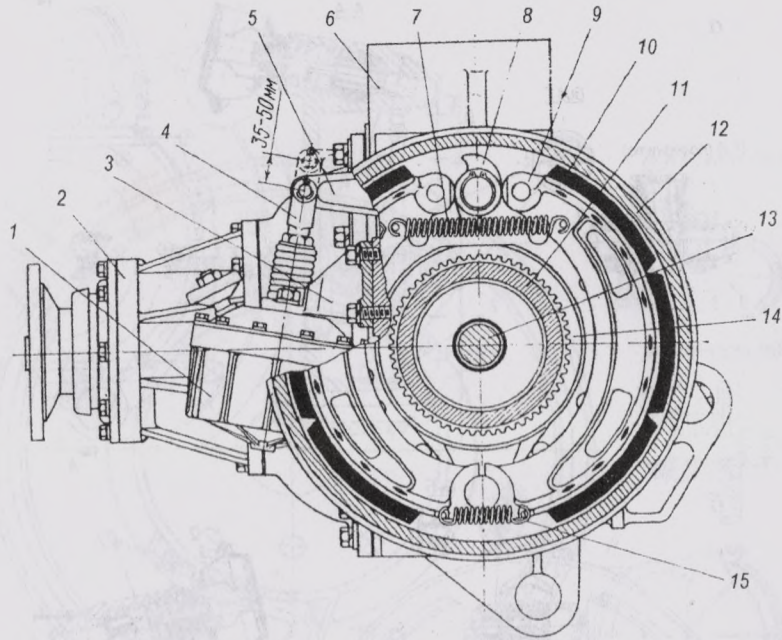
Тормоз автомобиля БелАЗ 7540: 1 – цилиндр; 2 – главная передача; 3 – кронштейн крепления цилиндра; 4 – вилка; 5 – рычаг; 6 – картер заднего моста; 7, 15 – пружины; 8 – разжимной кулак; 9 – колодка; 10 – фрикционная наклад-ка; 11 – кожух полуоси; 12 – барабан; 13 – полуось; 14 – суппорт
